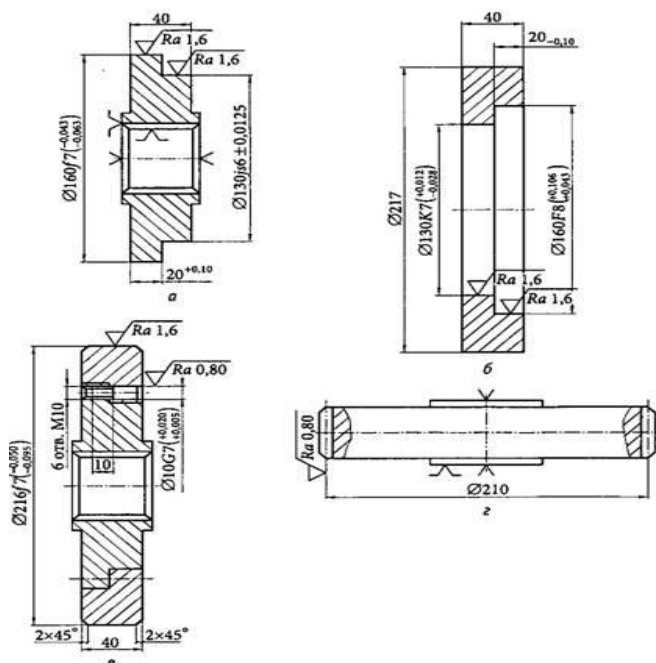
Технологический маршрут восстановления зубчатого колеса: а – срезание изношенного зубчатого венца; б – вытачивание заготовки нового зубчатого венца; в – установка нового зубчатого венца на ступицу; г – нарезание зубьев
